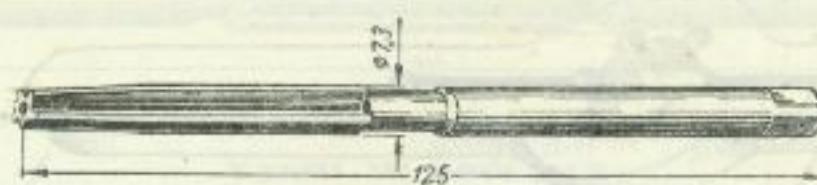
Развёртка для развёртывания отверстий под ВДП-И повышенную ось крышки ПМ-2.
